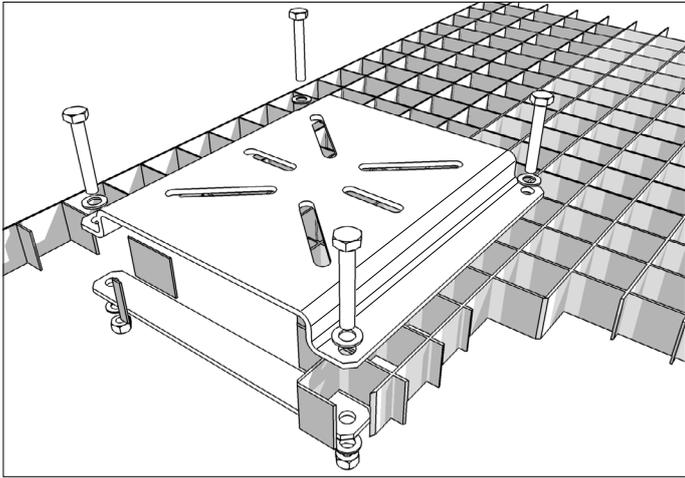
Montage de la plaque de montage pour étau d'établi
